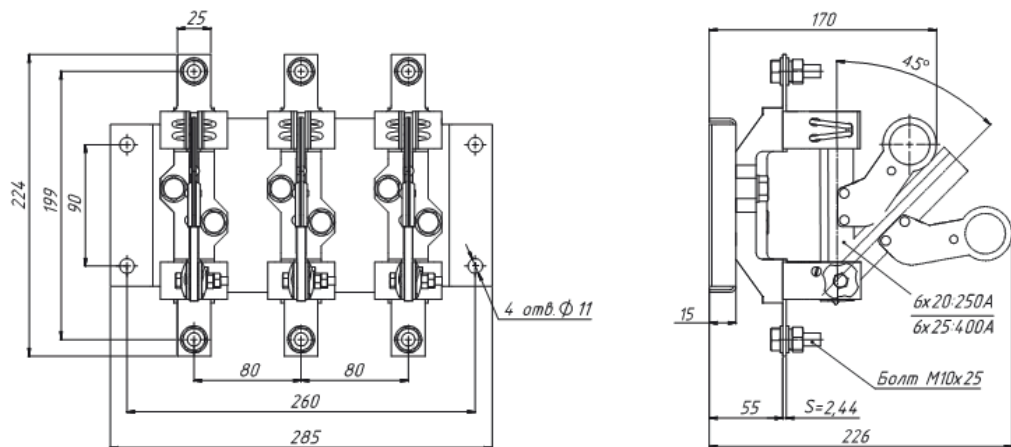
Разъединитель РЕ19-35(37)-31120-00 УХЛ3 с боковой рукояткой
